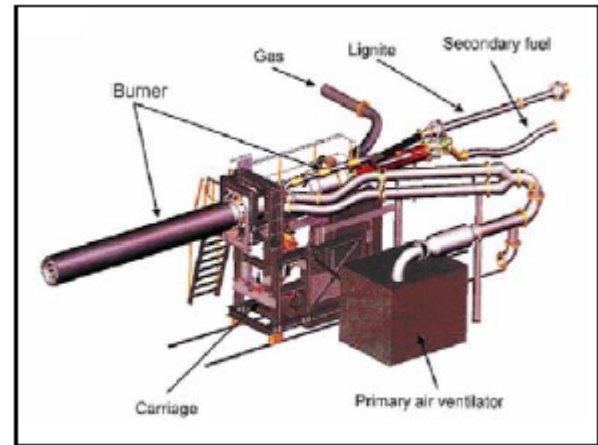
Устройство горелки для вращающейся печи [50, 51]
